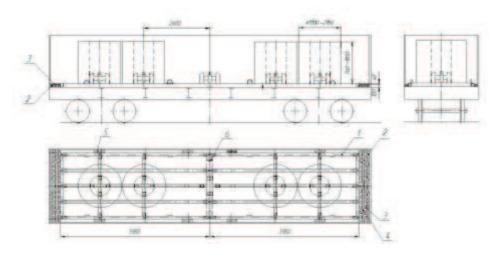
1 – рама; 2 – упорный брусок; 3 – скрепляющая доска; 4 – гвоздь; 5 – распорный брусок; 6 – увязка
